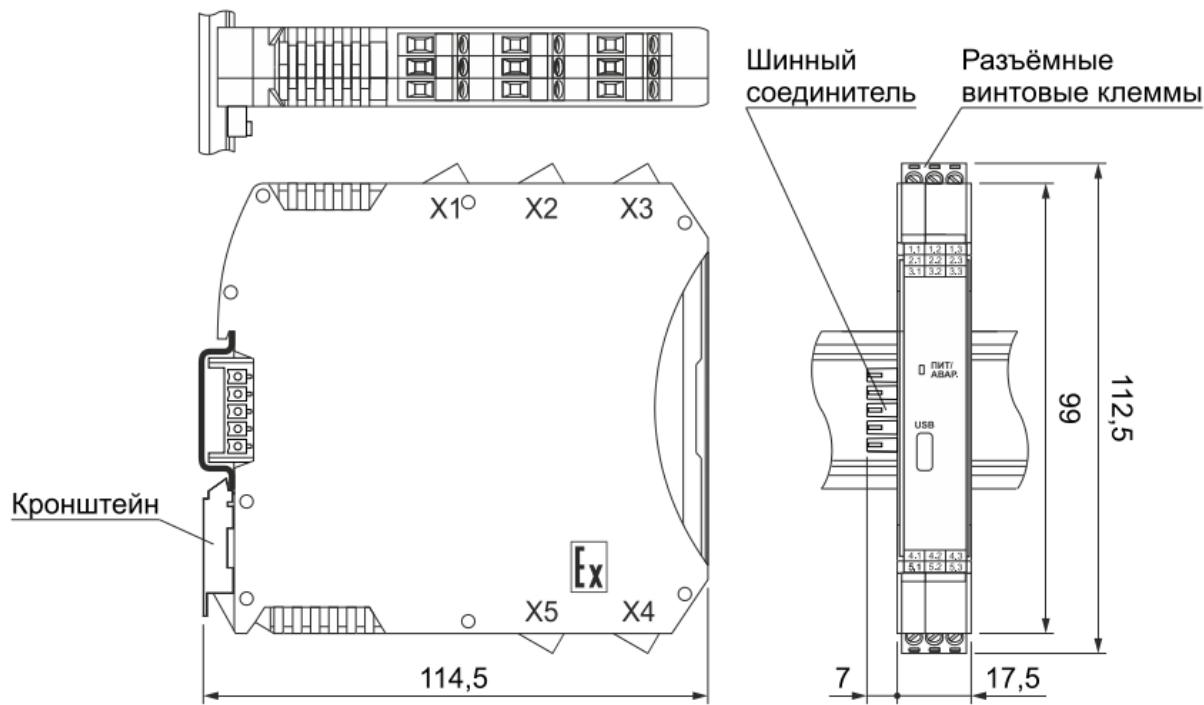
Габаритные размеры барьера KA5003Ex-NN
